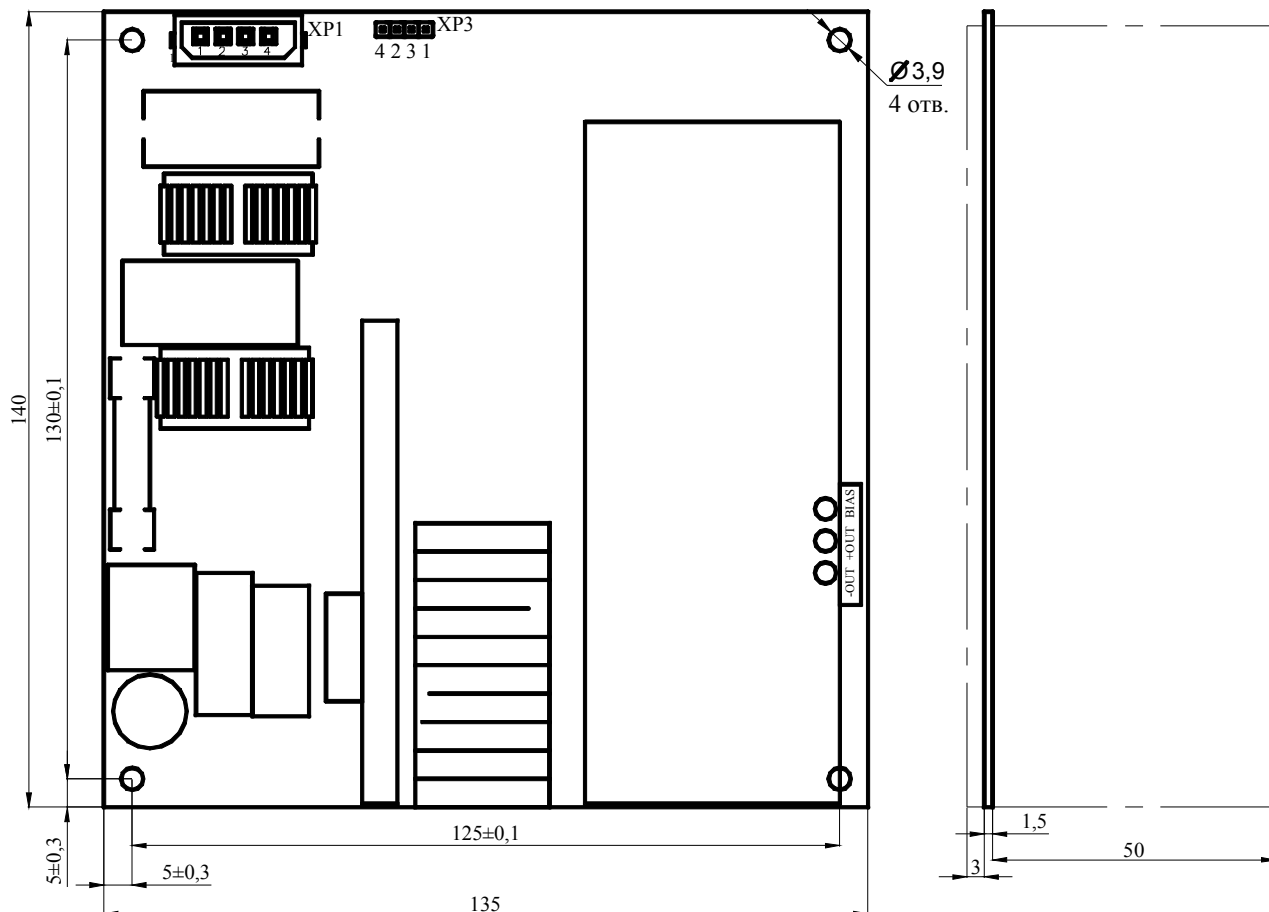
Габаритный чертеж корректора КМС600М
